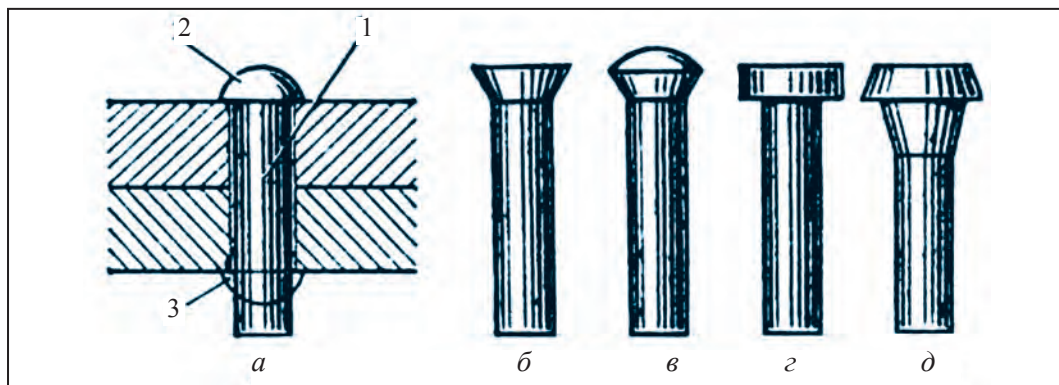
Виды заклёпок: а) с полукруглой головкой; б) со скрытой головкой; в) с полускрытой головкой; г) с плоской головкой; д) с конусовидной головкой; 1 – стержень заклёпки; 2 – верхняя головка; 3 – закрывающая головка.
